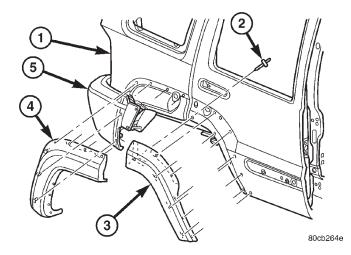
MOLDURAS DEL ENSANCHAMIENTO DEL HUECO DE LA RUEDA TRASERA
